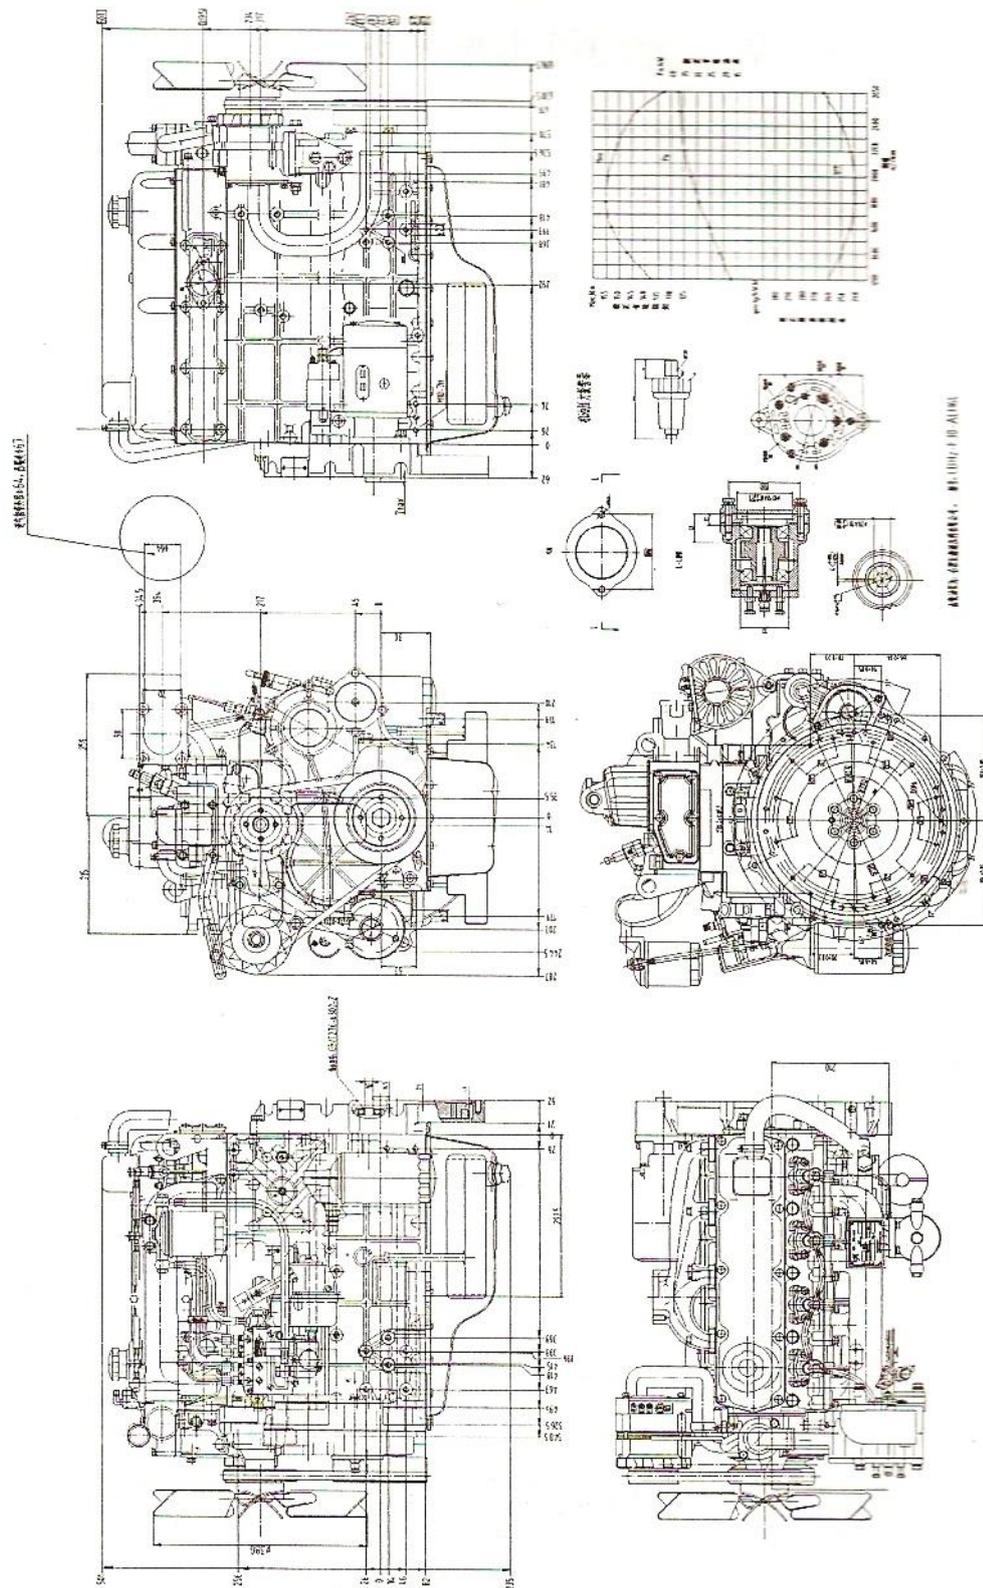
Внешний вид двигателя YCD4A12T (1AG004)
